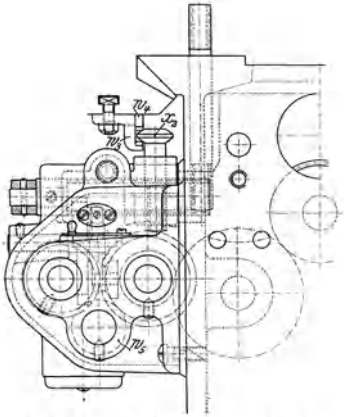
Ansicht des Wendegetriebes für die Supportbewegungen.
